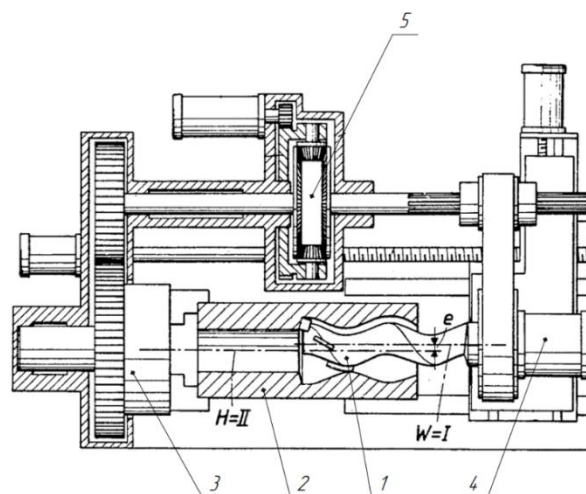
Эксцентриковое сверление: 1 – профилирующий инструмент; 2 – обойма-заготовка; 3 – привод заготовки; 4 – привод инструмента; 5 – синхронизирующий привод;  $H$  – ось вращения заготовки;  $W$  – ось вращения инструмента;  $e$  – эксцентриситет вращения инструмента и заготовки
